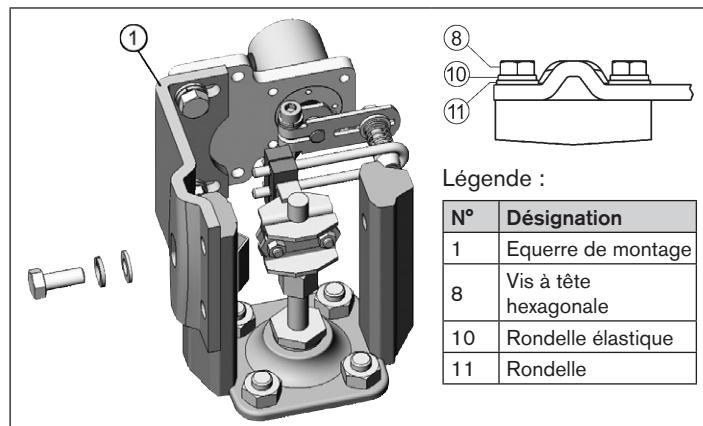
Fixer l'équerre de montage sur le cadre en fonte
